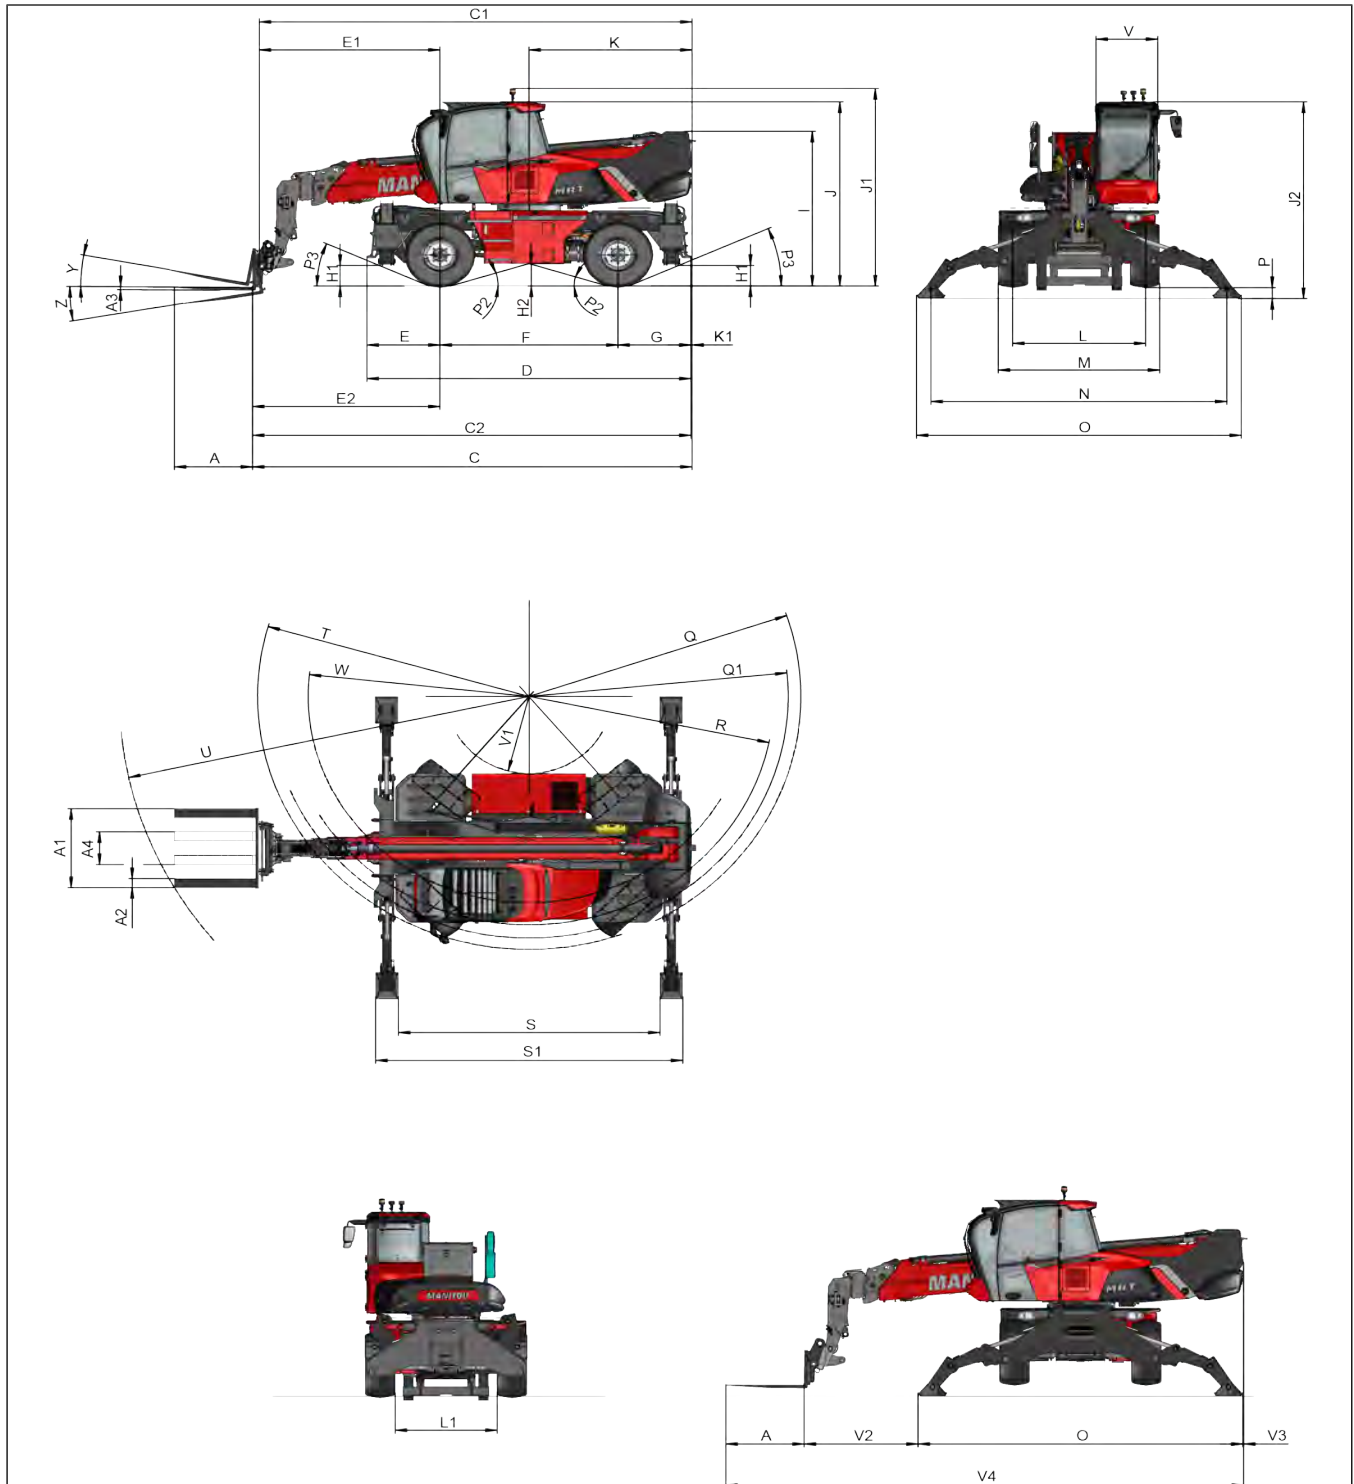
Dimensions (vue latérale, vue de face et vue de dessus)
